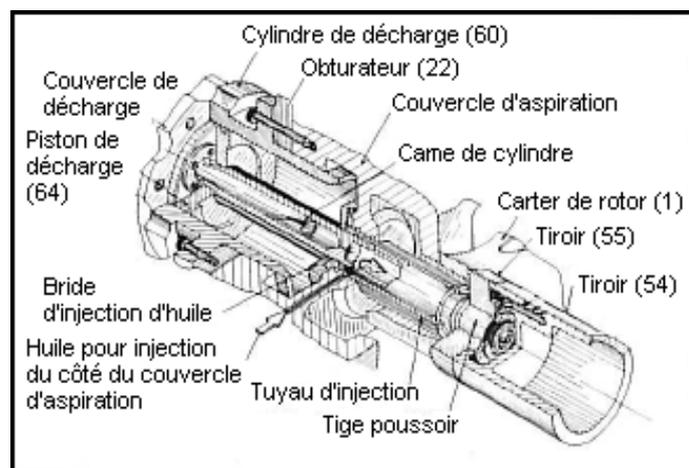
Tuyaux d'injection d'huile, vue explosée
